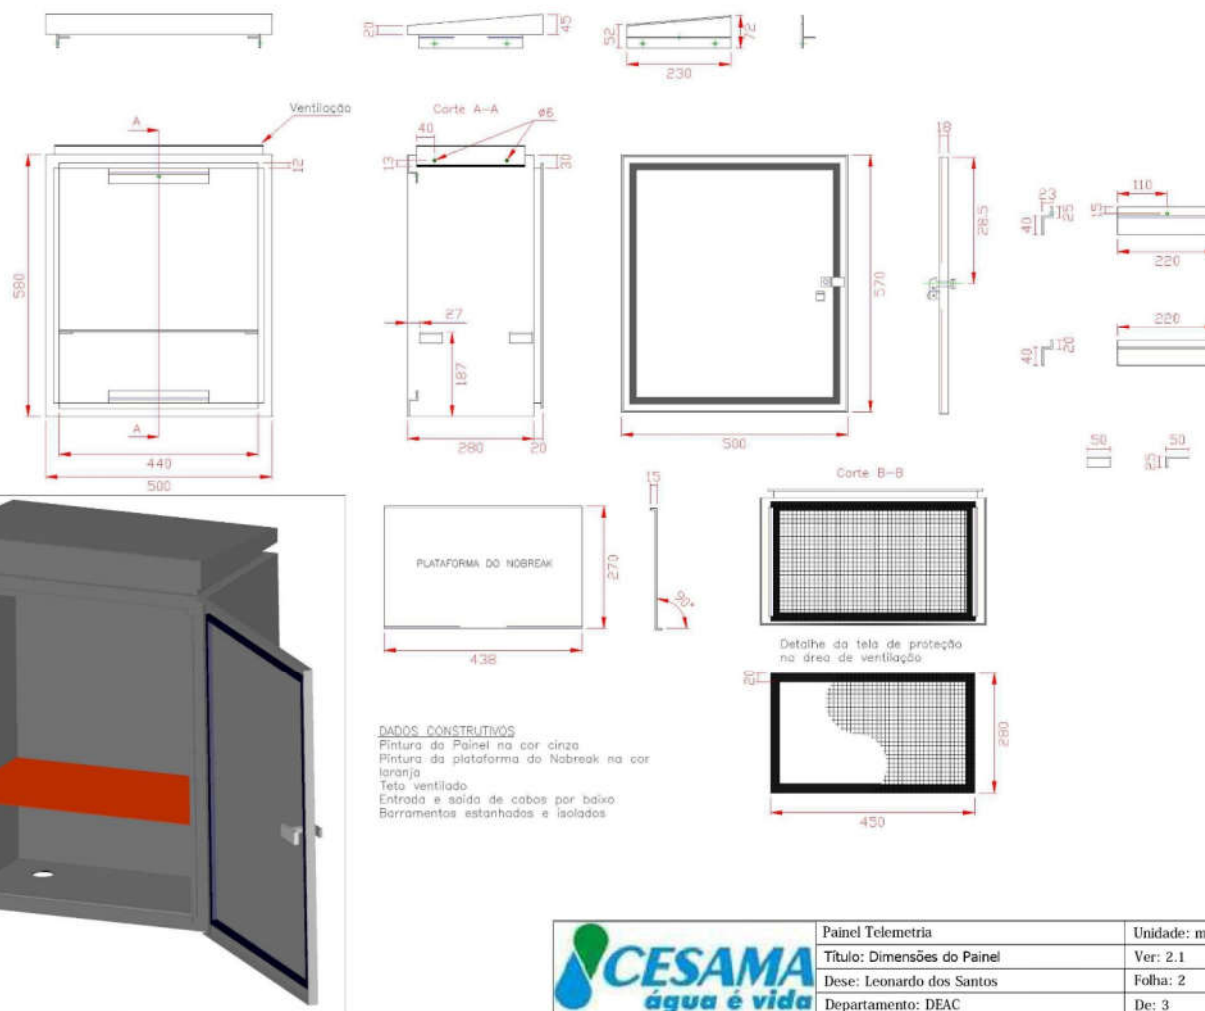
Detalhes construtivos painel de telemetria padrão CESAMA
